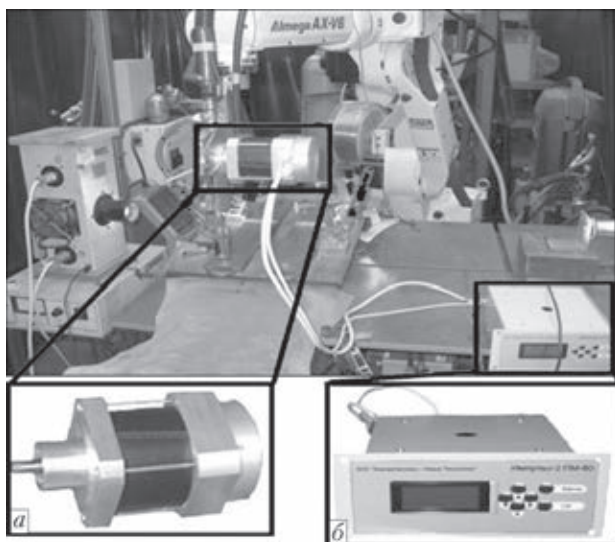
Механизм импульсной подачи электродной проволоки, установленный на сварочный робот: а — вентильный электродвигатель; б — блок управления привода
